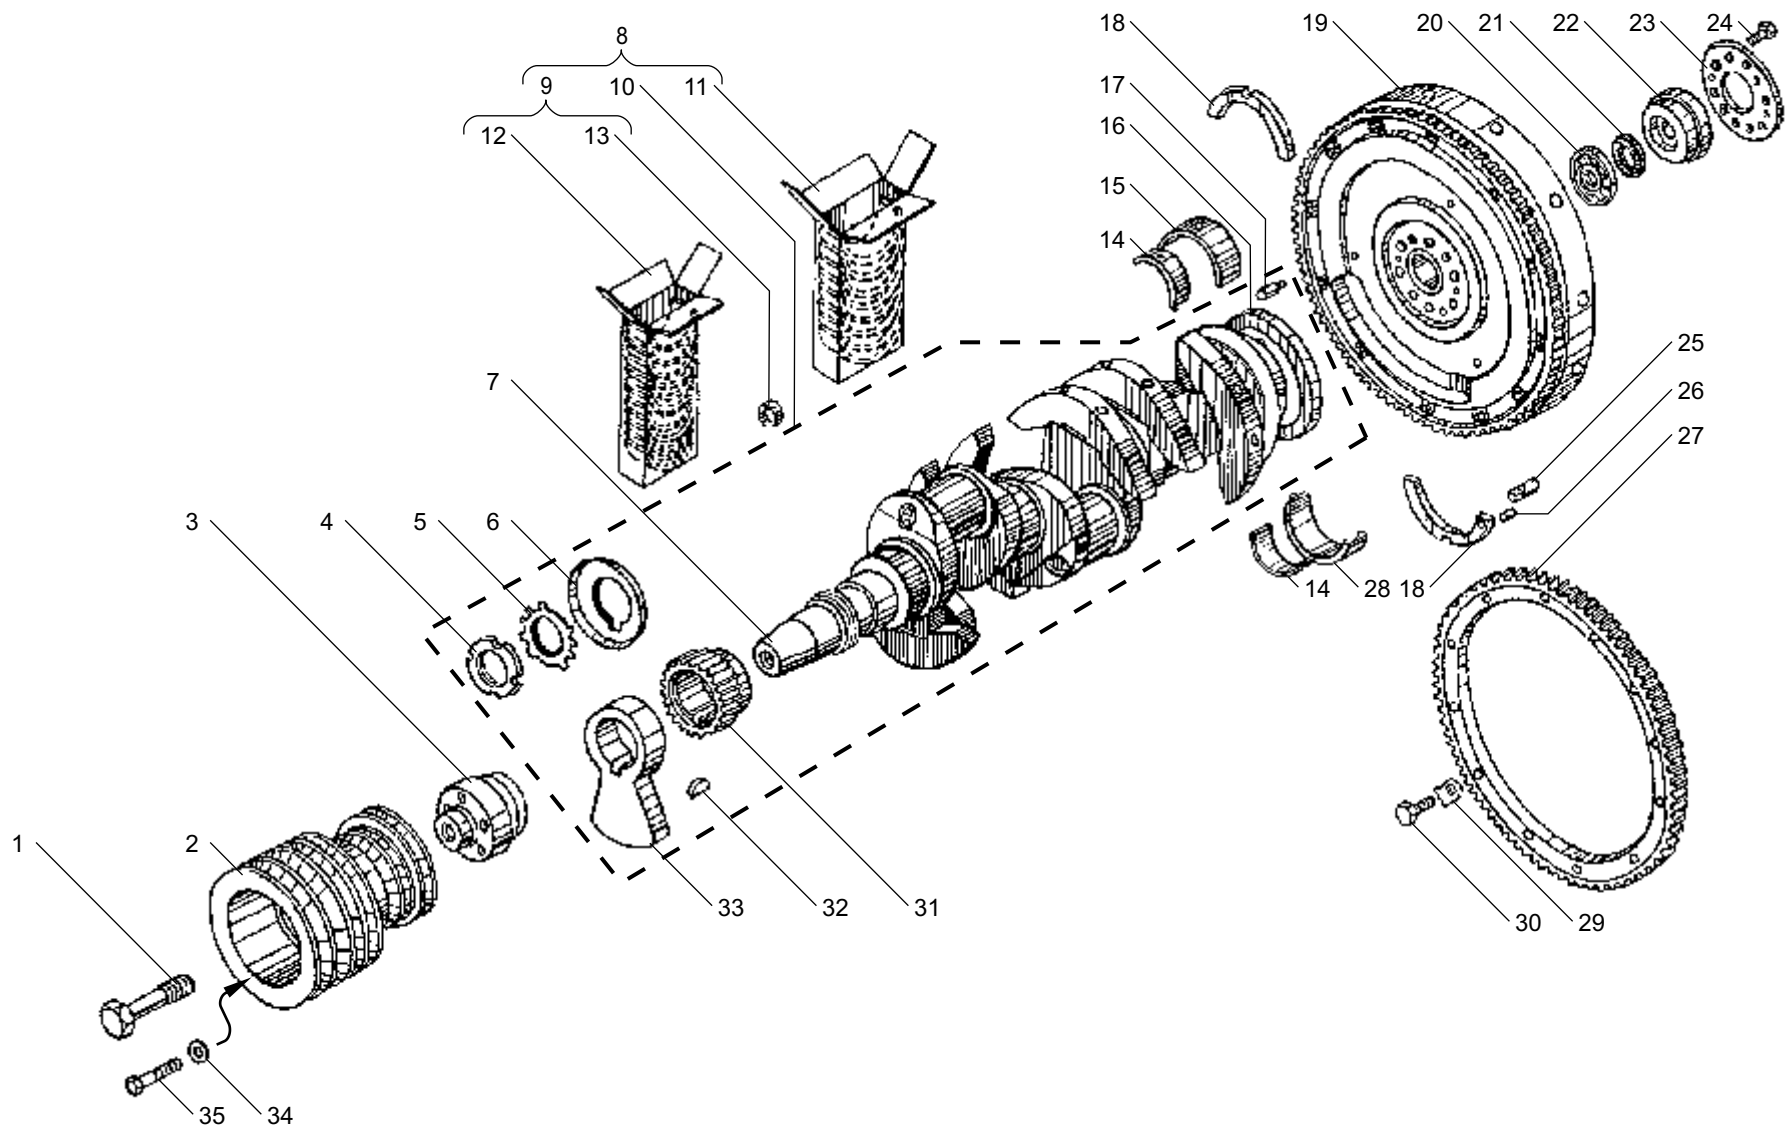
ВАЛ КОЛЕНЧАТЫЙ И МАХОВИК двигателя ЯМЗ-7601.10-01
